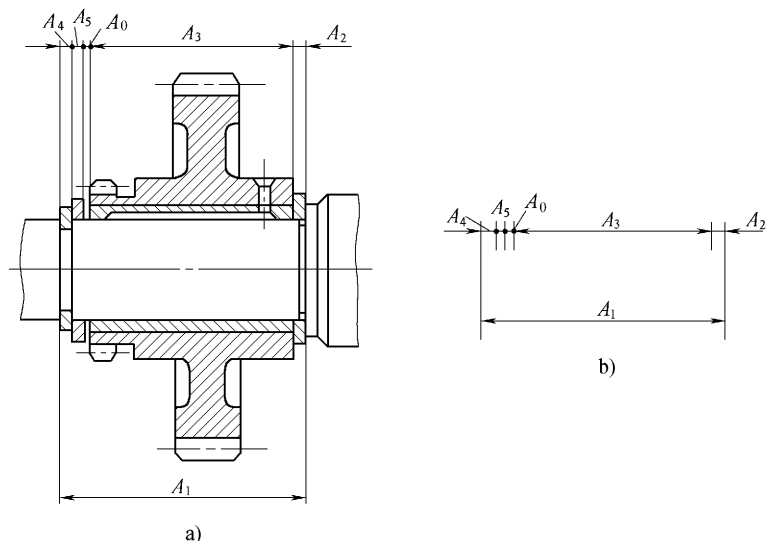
车床主轴大齿轮的装配示意图及装配尺寸链图
